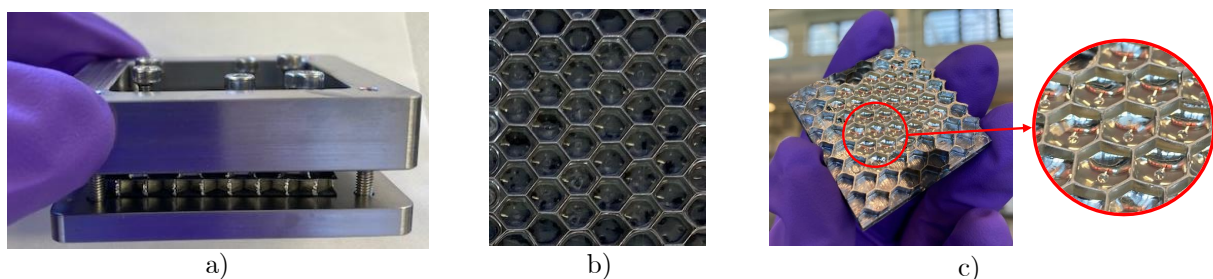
Prototypage d'un module de 30 unités (40x40 mm²) : a) Procédé de moulage, b) Optique moulée, c) Module avec revêtement argenté réfléchissant.
